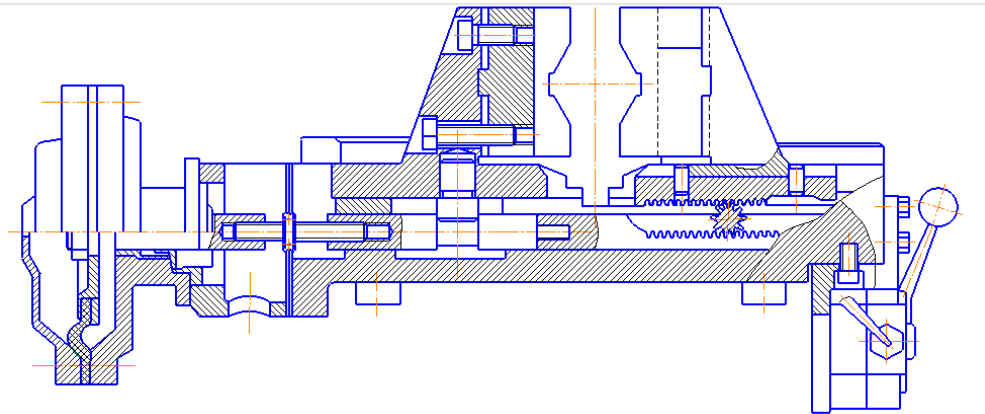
Пристрій для фрезерування шпонкових пазів
